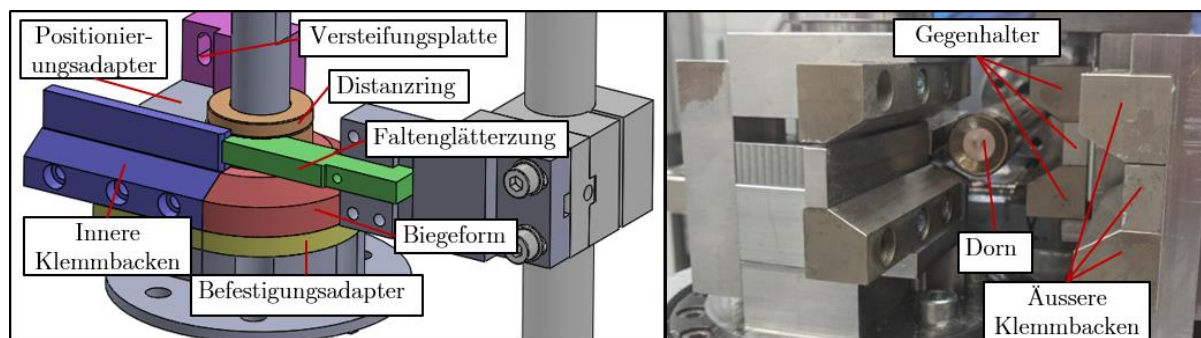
Aufbau geometrisch flexibler Biegewerkzeuge auf der RBV 35
